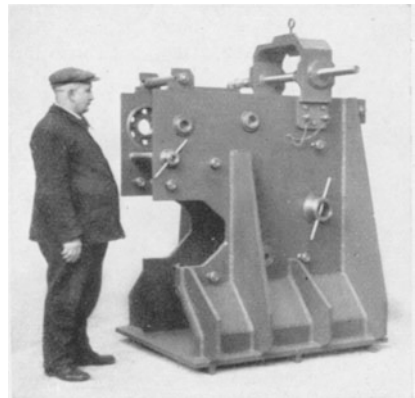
Geschweißte Bohrvorrichtung.
